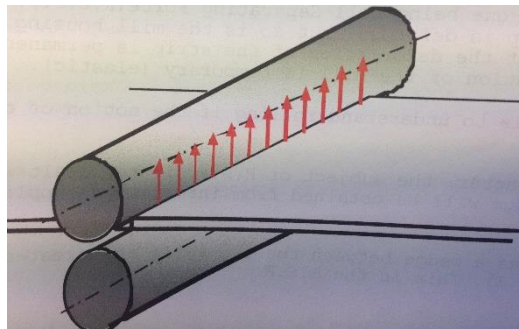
Fuerza principal que sufren los rodillos en el proceso
